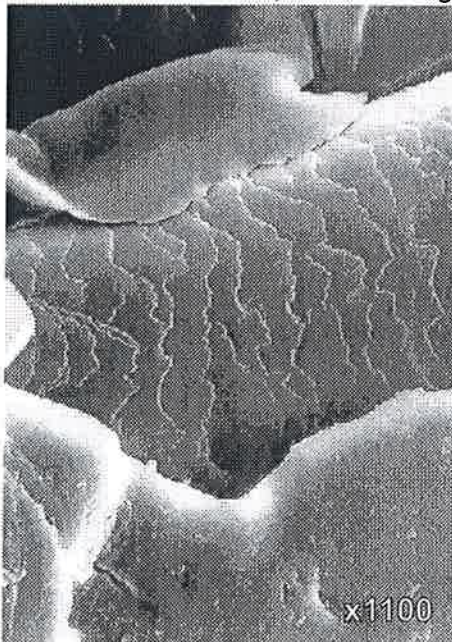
Detailausschnitt aus Bild 2, 1100-fach vergrößert
